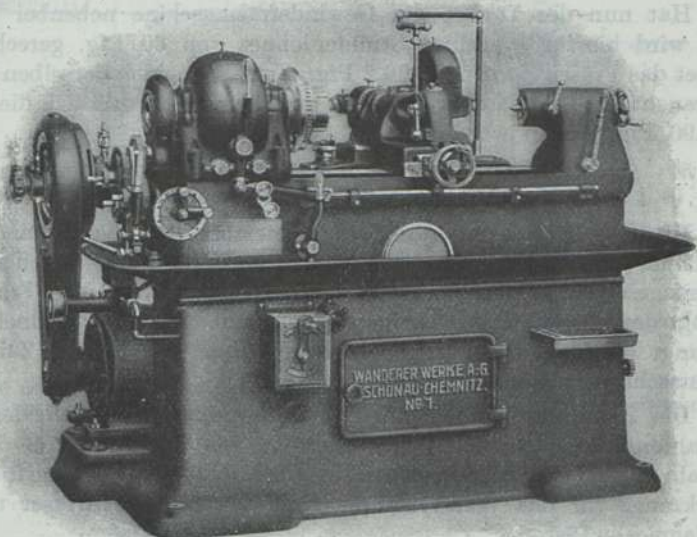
Gewindefräsmaschine der Wanderer-Werke, Chemnitz.
